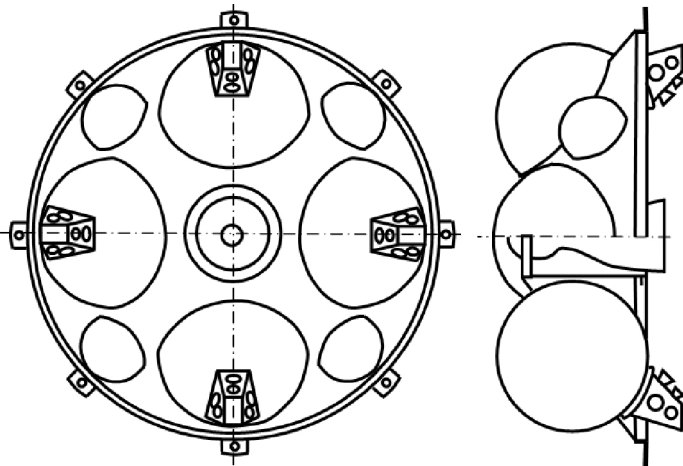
Компонировочная схема комплексной двигательной установки с передачей усилия на нижнюю часть приборно-агрегатного отсека
